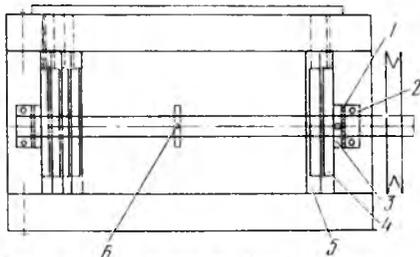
Измельчитель (вид сверху): 1 — уплотнитель; 2 — шариковый подшипник; 3 — шайба со штифтом; 4 — прокладка; 5 — диск; 6 — штифт (Ø 2,5)
